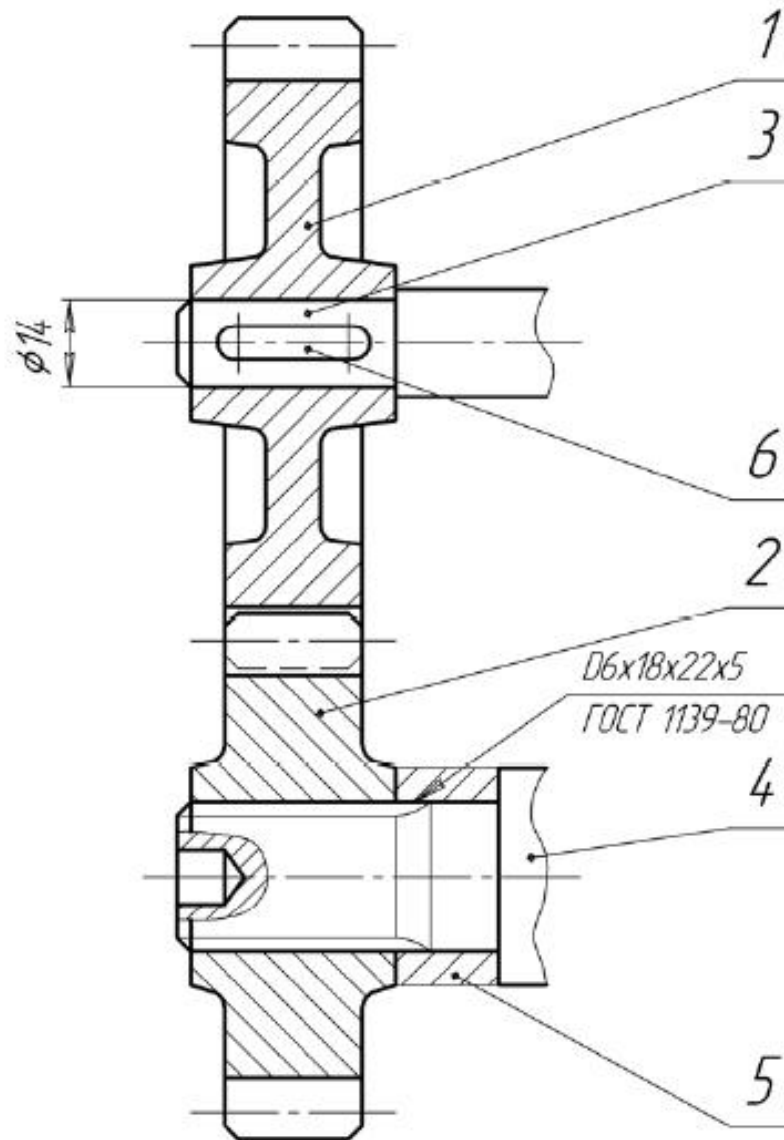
Рабочий чертеж шестерни со шлицевым отверстием
